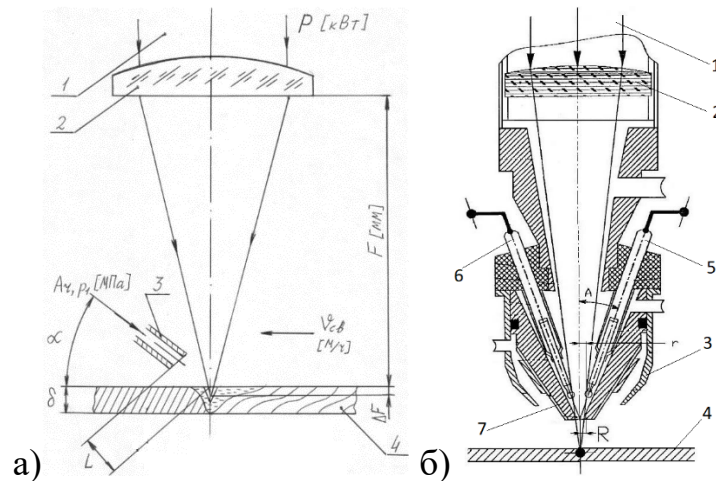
Технологічні схеми процесів лазерного , а) та лазерно-мікроплазмового б) зварювання: 1 – лазерне випромінювання; 2 – фокусуюча лінза; 3 – сопло подачі захисного газу; 4 – зразок; 5, 6 – електроди; 7 – плазмоутворююче сопло
